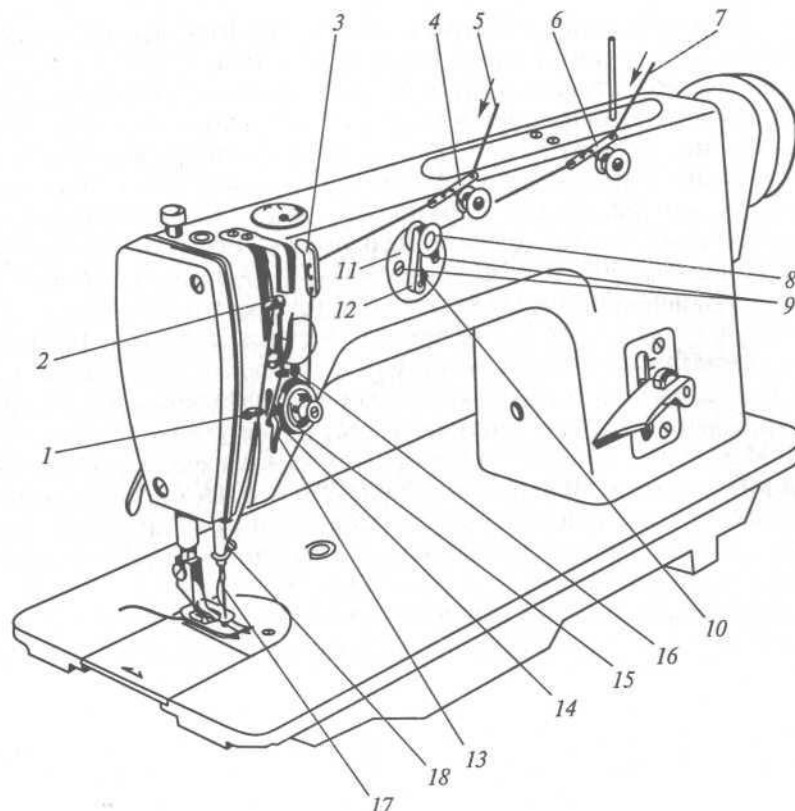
Схема заправки голкової нитки на машині 1022М
